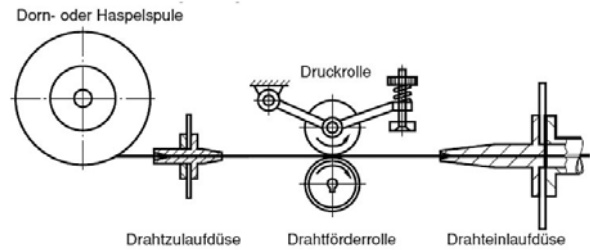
Einlegen der Drahtrolle, Drahtführung
